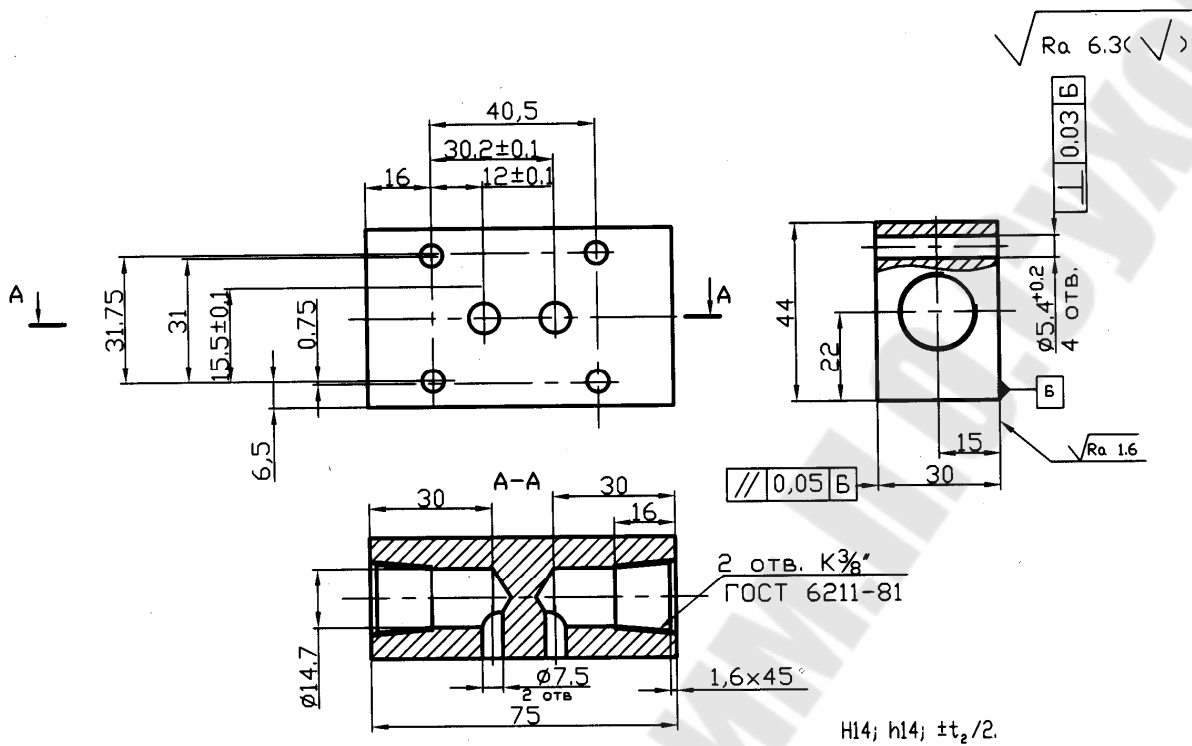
Корпус. Сталь 45 ГОСТ 1050-74.
